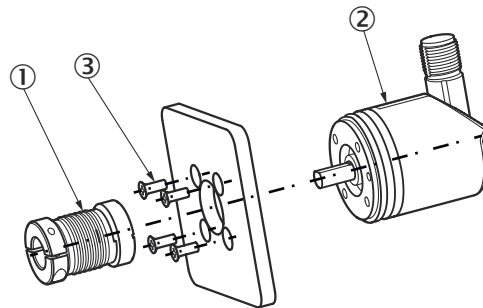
Anbau über flanschseitige Gewindebohrungen
